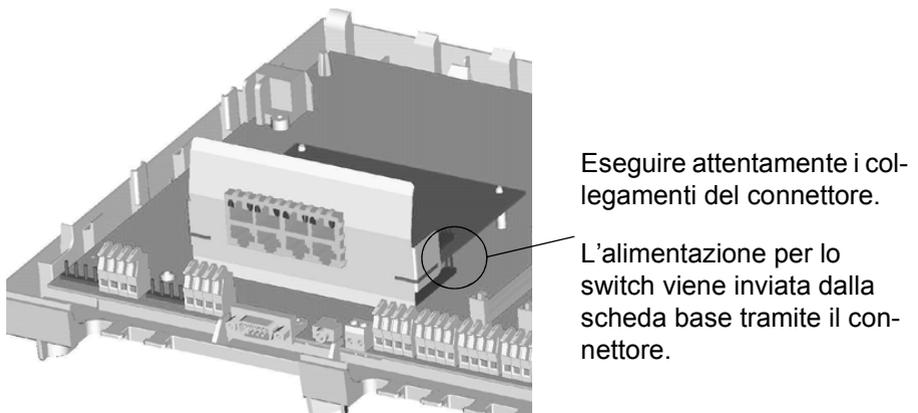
Montaggio del set di upgrade sulla scheda base
